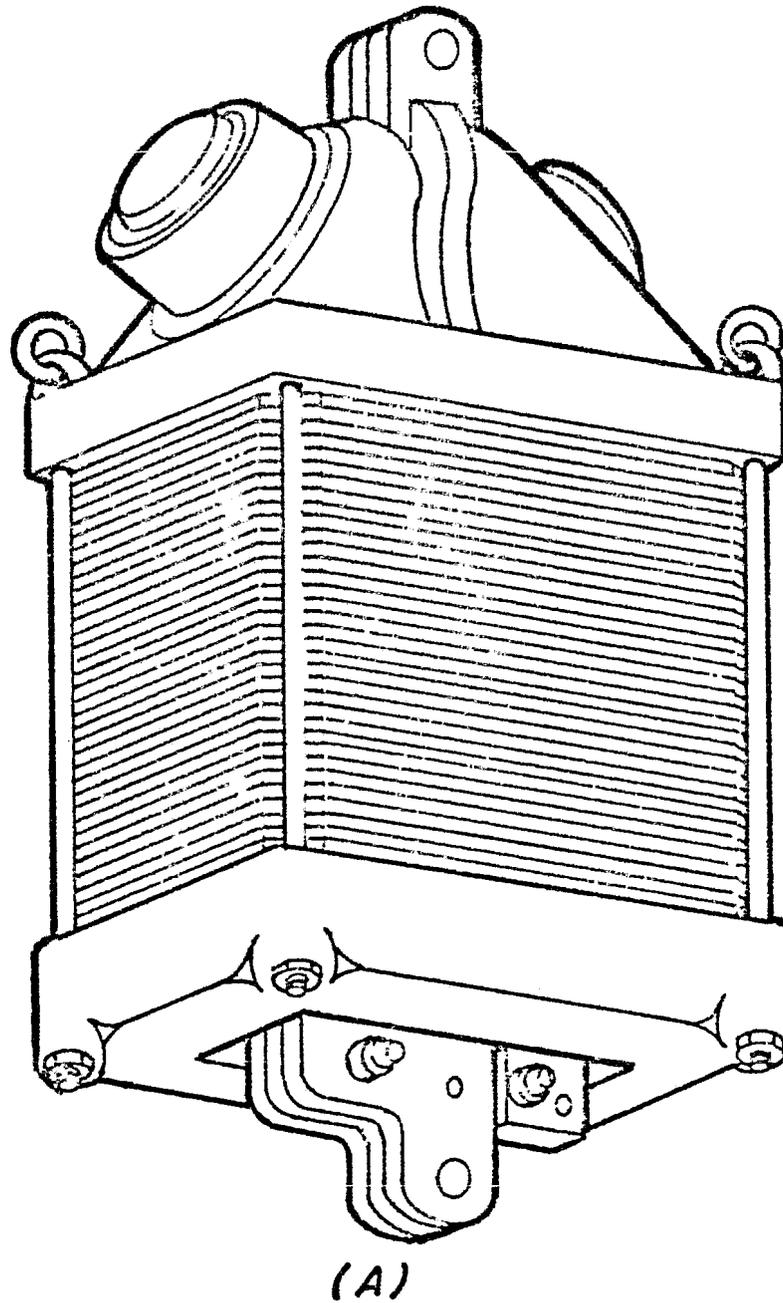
CONSTRUCCION DE UN TIPICO TRANSFORMADOR PARA PISTOLA DE SOLDAR.
